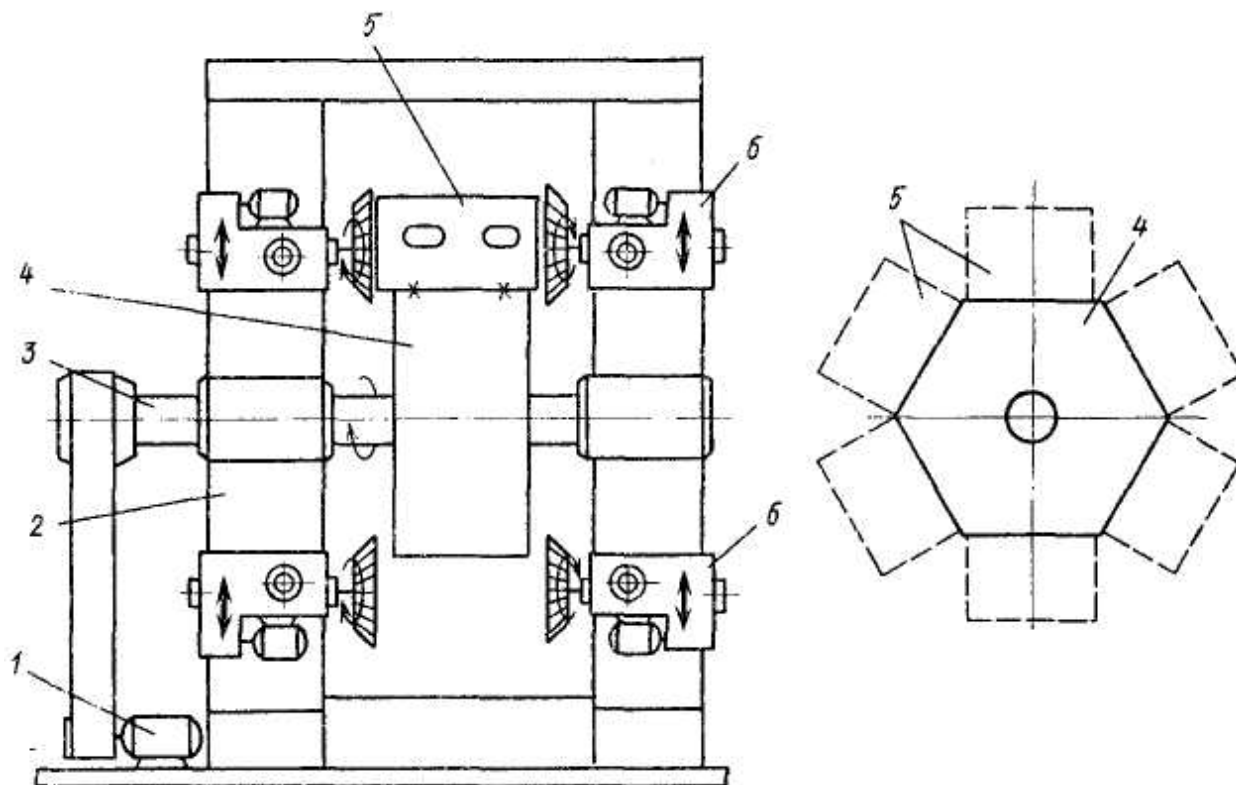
Принципиальная схема барабанно-фрезерного станка: 1 – электродвигатель; 2 – стойки; 3 – вал; 4 – барабан; 5 – заготовка; 6 – фрезерная головка
